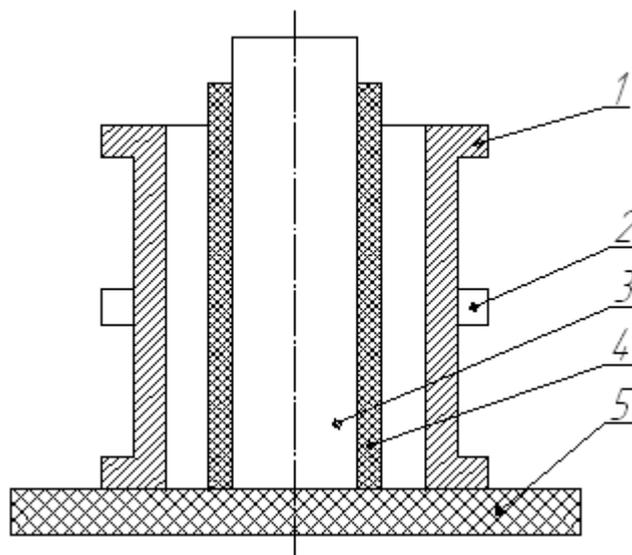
Подшипник скольжения с разъемным корпусом
